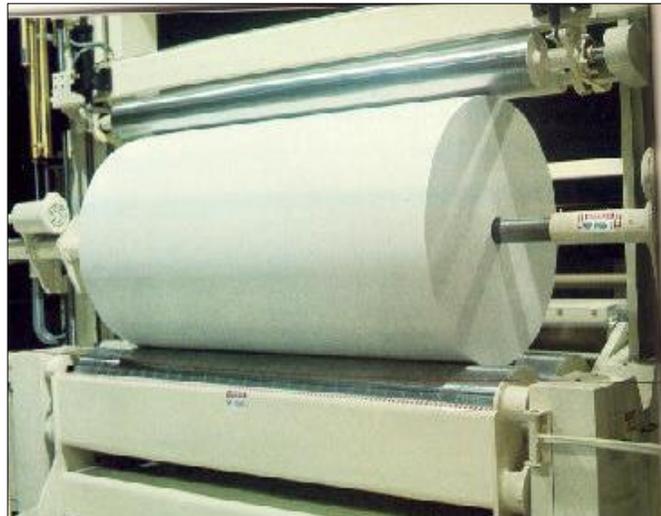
Rodillo Jinete en Bobinadora de Dos Tambores.
